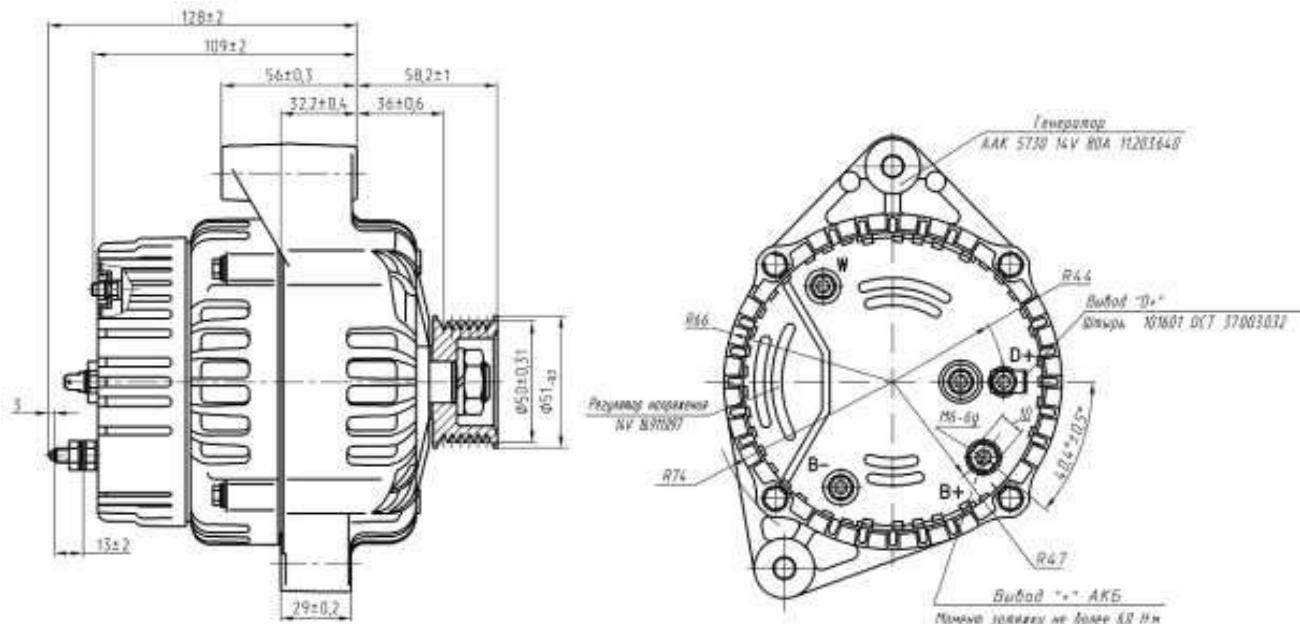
Габаритные размеры генератора 3212.3771000-10 ОАО «БАТЭ»
